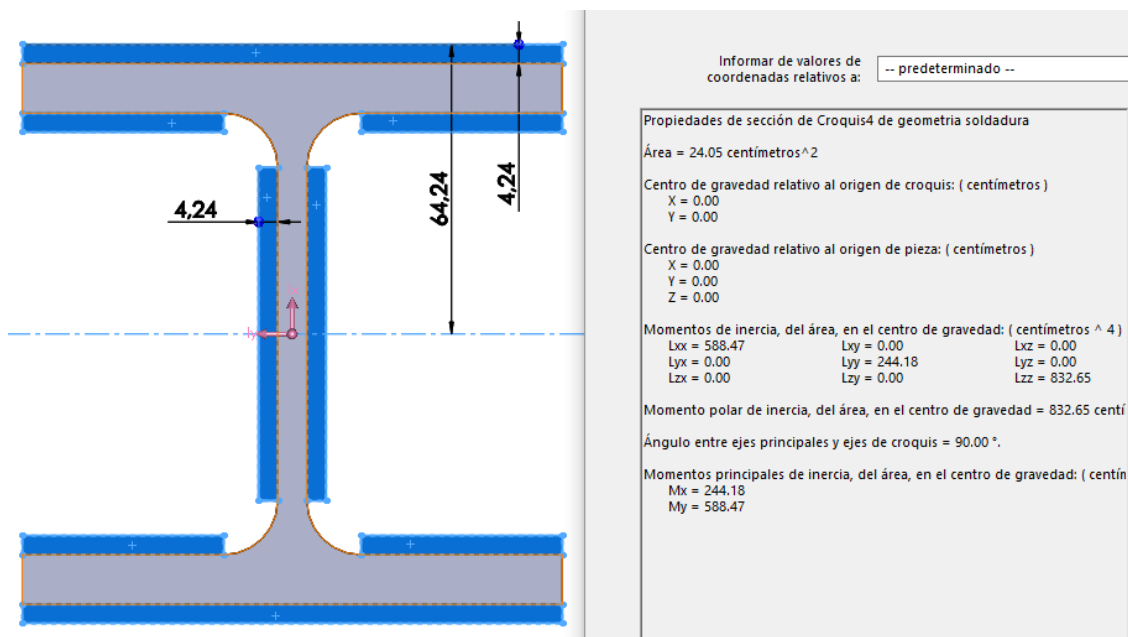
Propiedades de los cordones de soldadura
